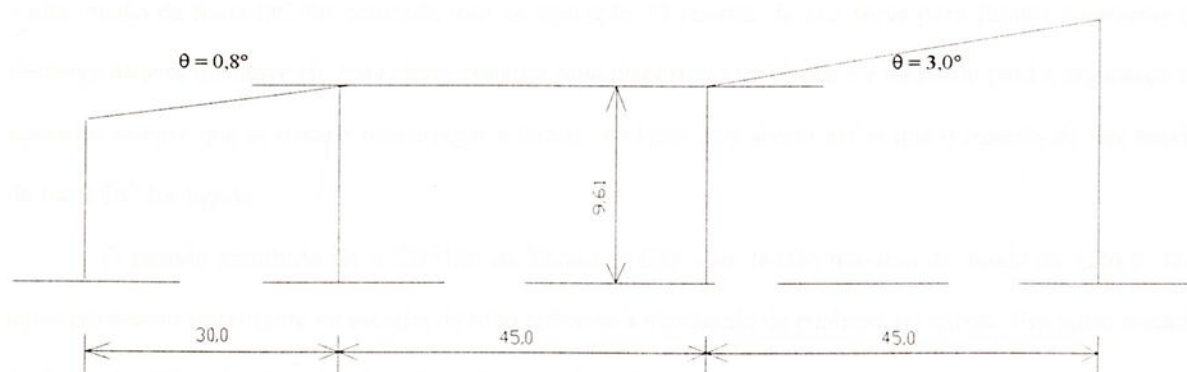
Perfil longitudinal do ressoador de cones truncados.
